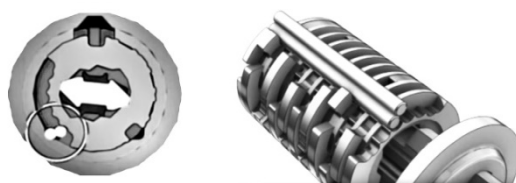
, рис. 5. Схематичне зображення прокручування циліндру в корпусі механізму (вид в розрізі та збоку)
